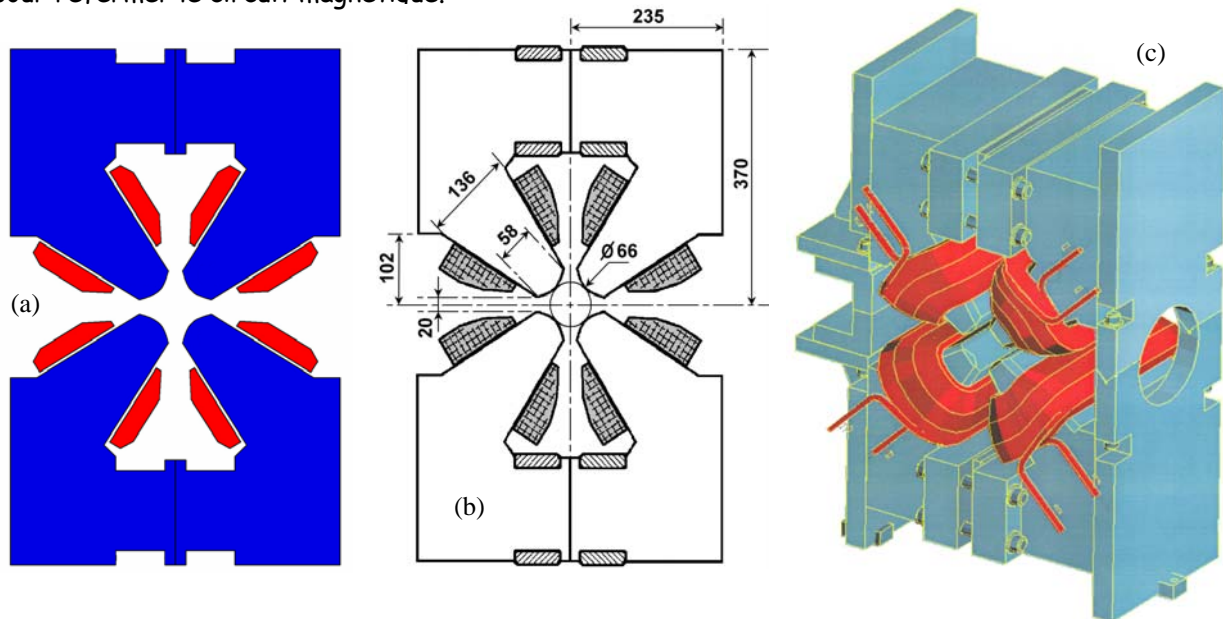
Section courante, (a) modèle TOSCA, (b) Dimensions principales, (c) Assemblage proposé pour l'APD
